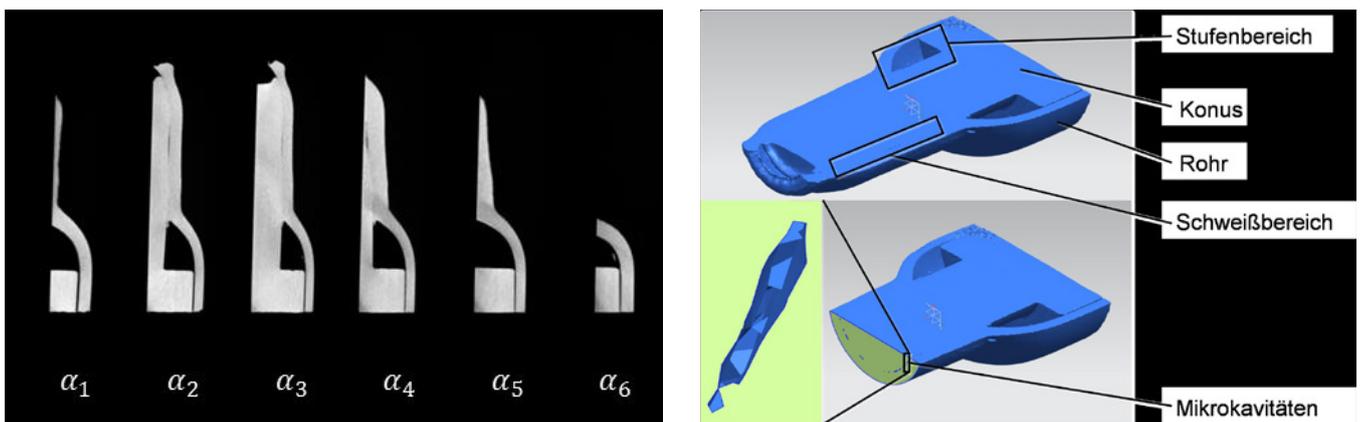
Röntgenbilder verschiedener Anstellwinkel einer magnetpulsverschweißten Probe und der mittels Postprocessing errechneten 3D-Darstellung
